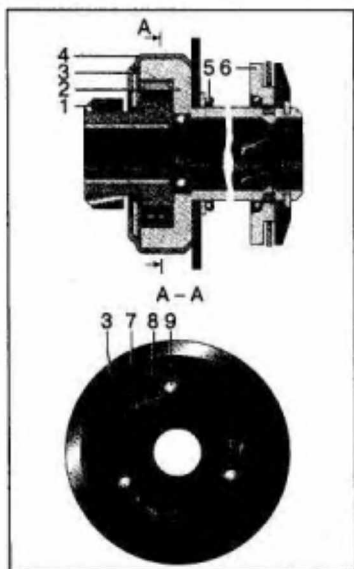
Муфта свободного хода: 1 — внутренняя обойма муфты; 2 — наружная обойма муфты свободного хода; 3 — держатель пружины; 4 — кожух муфты; 5 — буферная пружина привода; 6 — поводковое кольцо; 7 — пружина; 8 — толкатели; 9 — ролики
